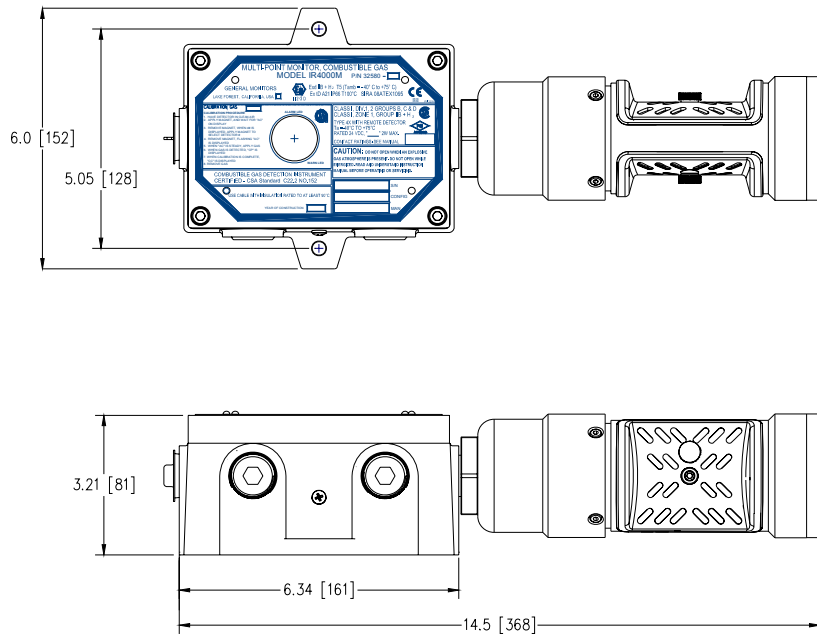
Dimensions d'ensemble de l'IR400 monté
